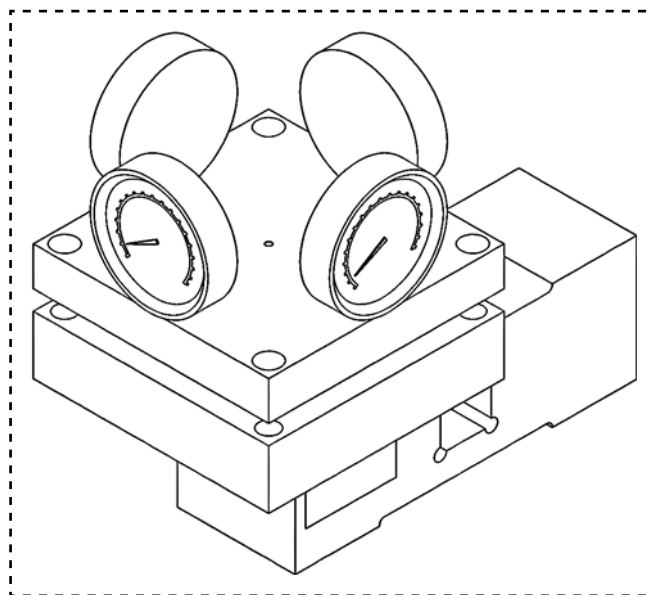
Элемент конструкции нагружения при экспериментальных исследованиях сверления отверстий в напряженно-деформированном материале заготовки
